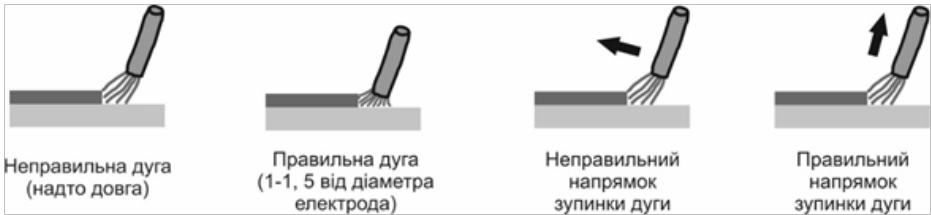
Відстань розташування електрода із покриттям до деталі під час ручного дугового зварювання (ММА).
